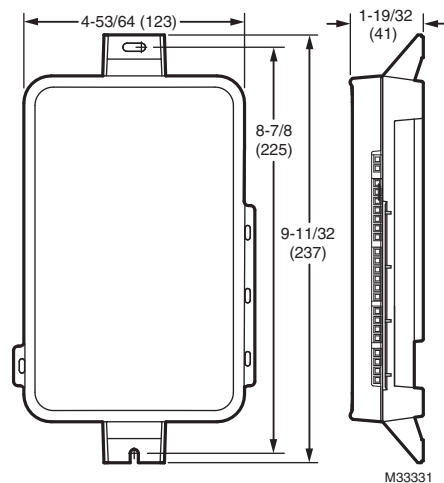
Dimensions du module d'interface d'équipement en po (mm)
